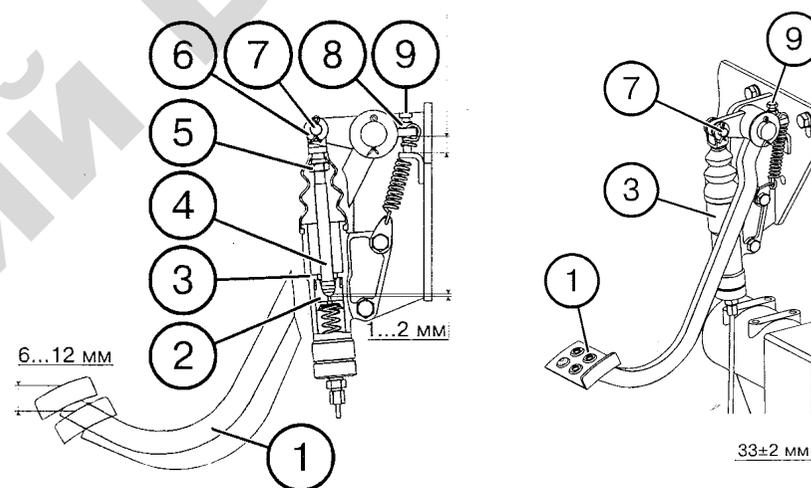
Регулировка рабочих тормозов трактора «Беларусь-1523»: *1* – педаль тормоза; *2* – поршень; *3* – главный тормозной цилиндр; *4* – толкатель; *5* – контргайка; *6* – вилка; *7* – палец; *8* – гайка; *9* – болт упорный
